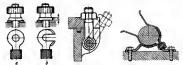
Guardacabo de Fig. 38. Tornillo Fig. 39. Pinza eliras
